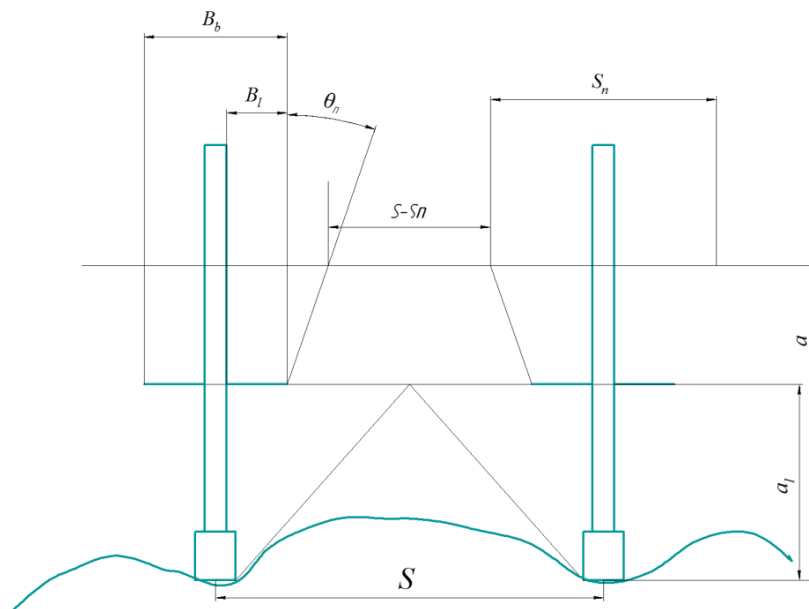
Розрахункова схема для визначення ширини робочого органу для внесення добрив
